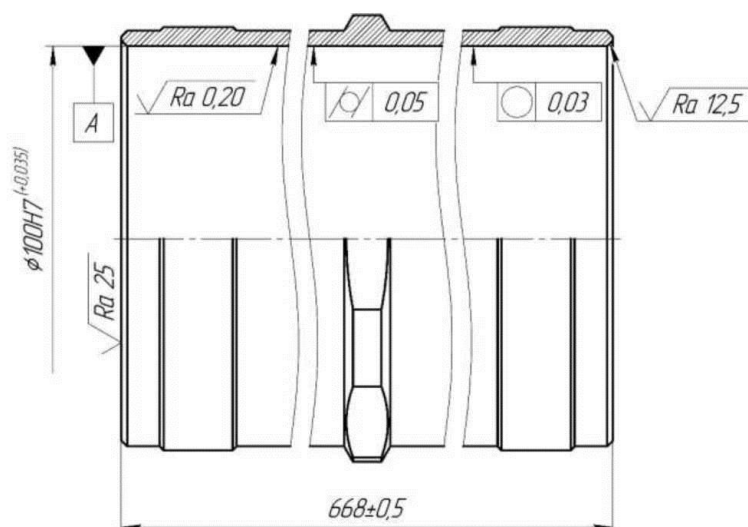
Типовая конструкция гильзы гидроцилиндра и предъявляемые к ней требования по точности и шероховатости
